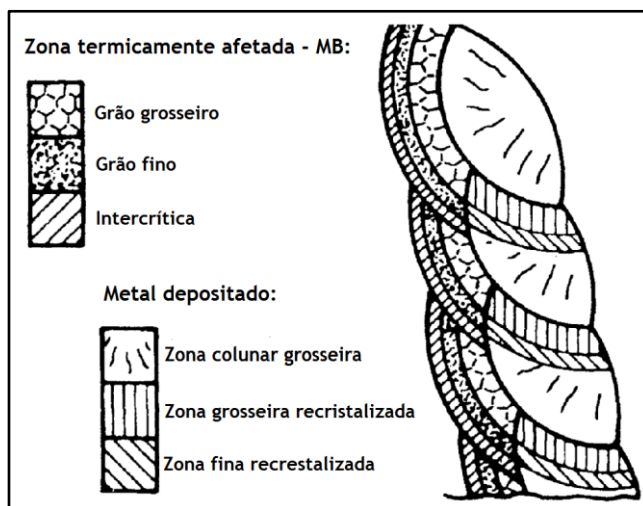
Microestrutura de uma soldadura multi-passes [38]
